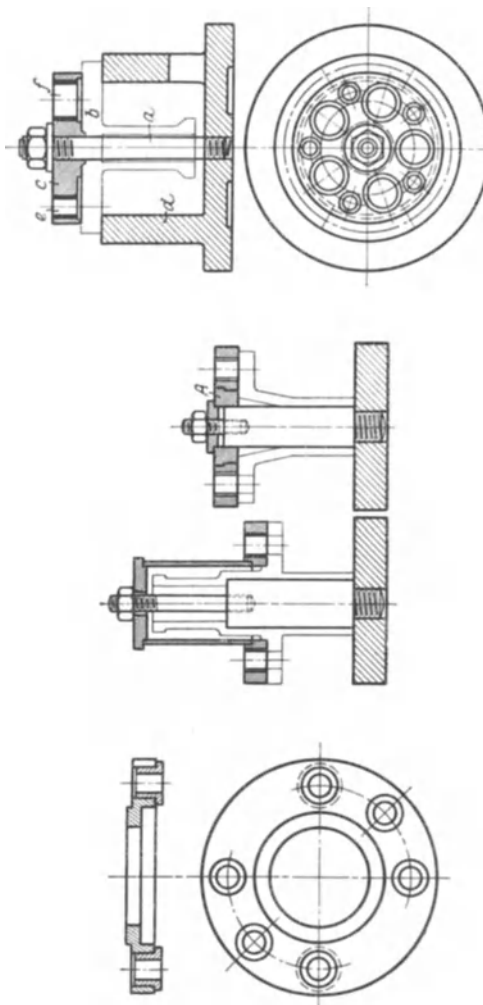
Bohrflansche oder Bohrplatten, die einfachste Art von Bohrvorrichtungen für Flansche.
